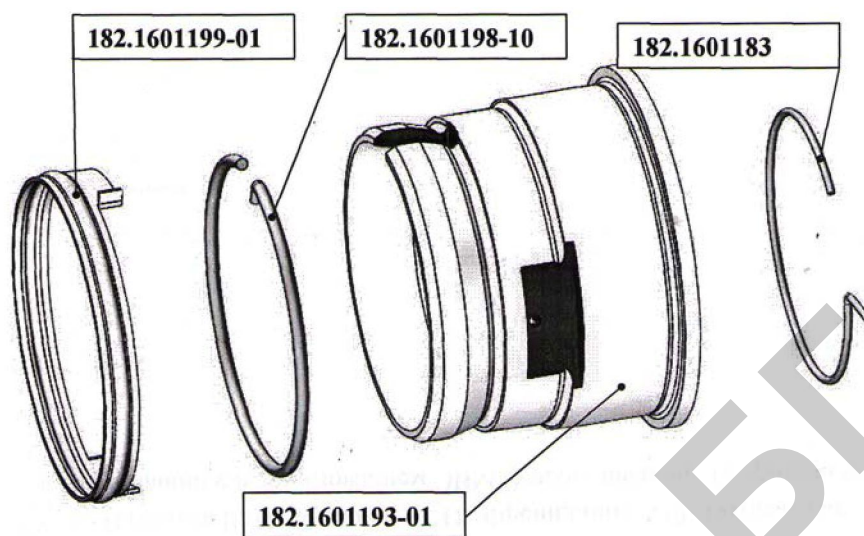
Внешний вид деталей муфты выключения сцепления:
